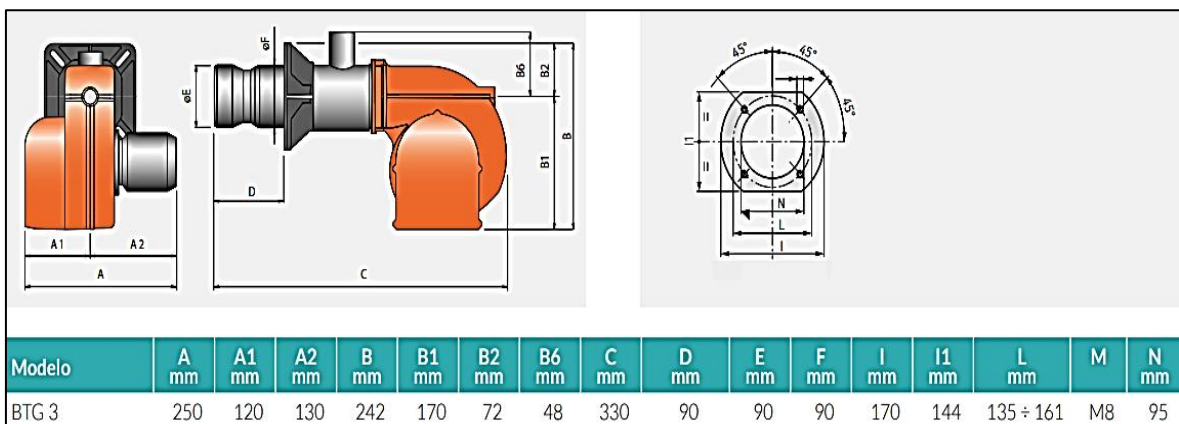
Dimensiones del quemador de gas para el horno pirolítico.
